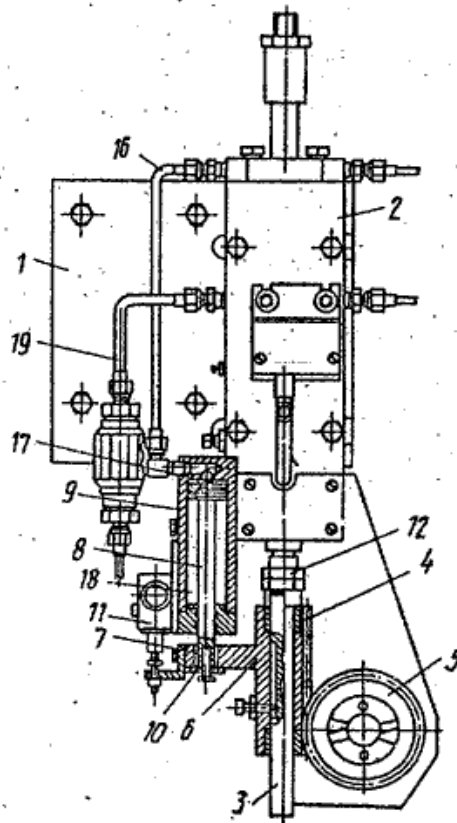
Привод подачі шпindelної головки свердлильного верстата.[15]
